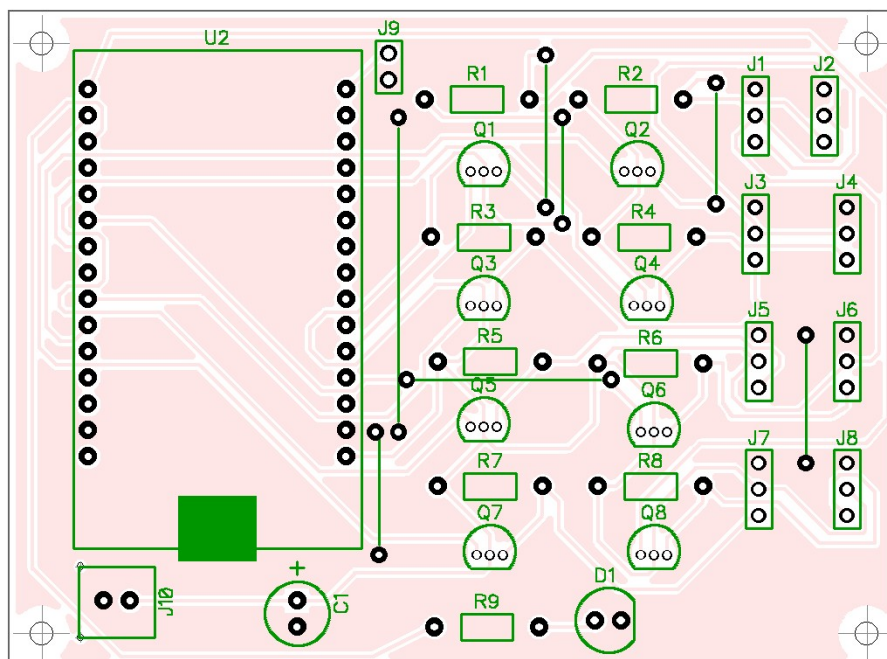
Parte superior do layout da PCB. Fonte: Própria
